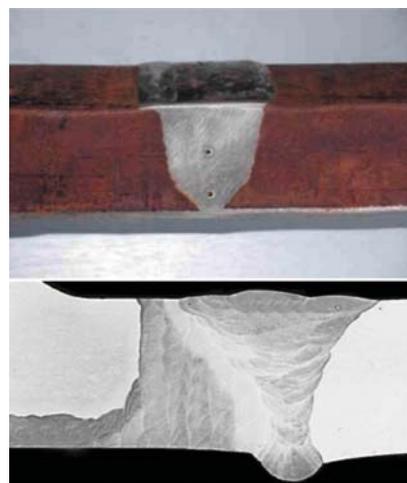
Плакированная труба со сварным соединением из коррозионно-стойкой стали (сверху) и сварной шов, соединяющий два различных материала — легированную и углеродистую сталь (снизу)
